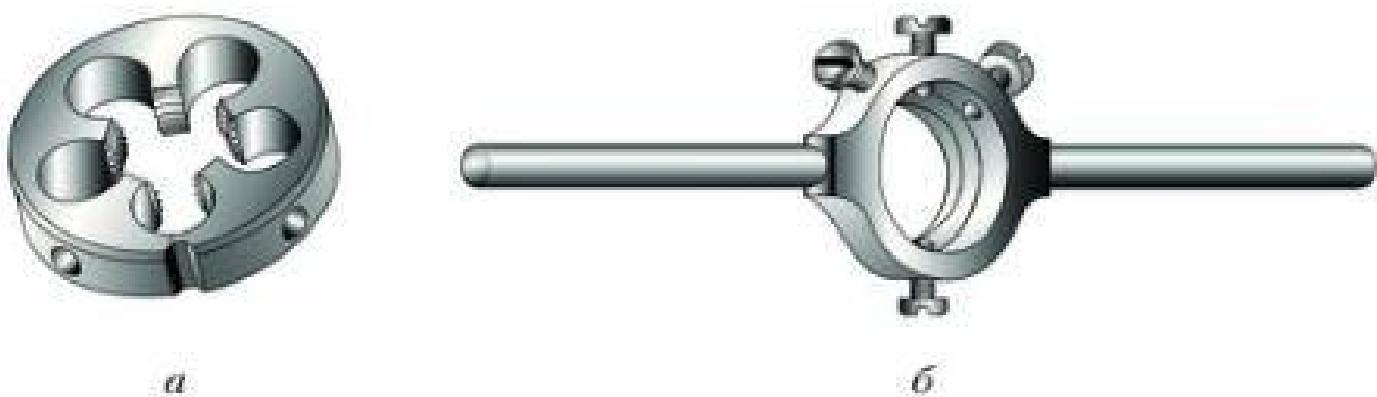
Круглая плашка (*а*) и плашкодержатель (*б*)
